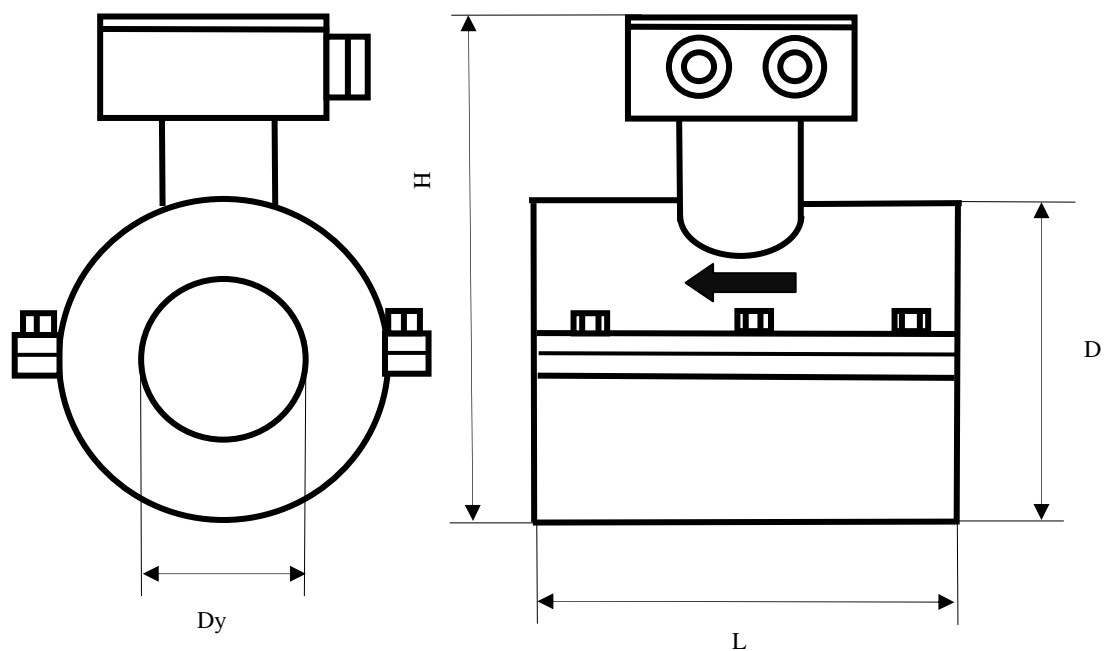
Габаритные размеры преобразователя ПРЭ -0114 модель 1
